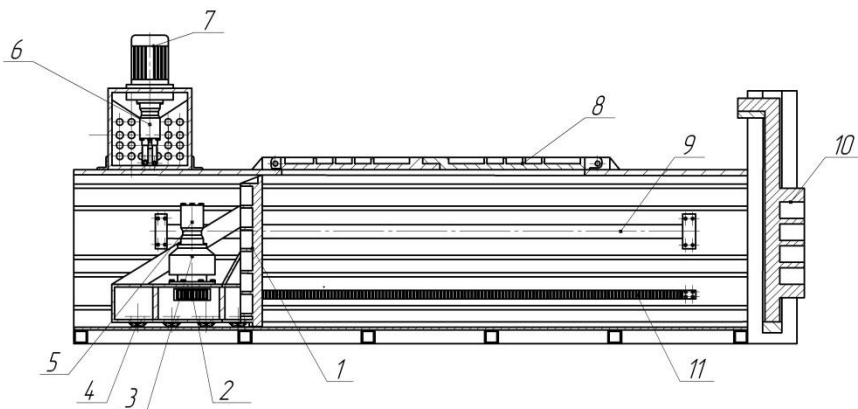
Пресс-контейнер для вторичных ресурсов с приводом пресс-платформы от двух гидромоторов
